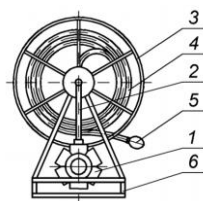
Схема устройства промывки дренажа 1 – насос, 2 – трубопровод, 3 – барабан, 4 – промывочный рукав, 5 – промывочная насадка, 6 – рама.
